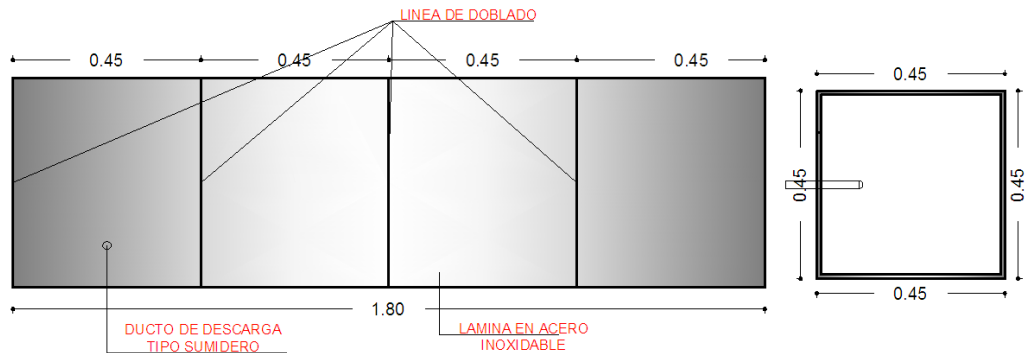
Vista zona de carga en perfil sin doblez y planta con doblez.
